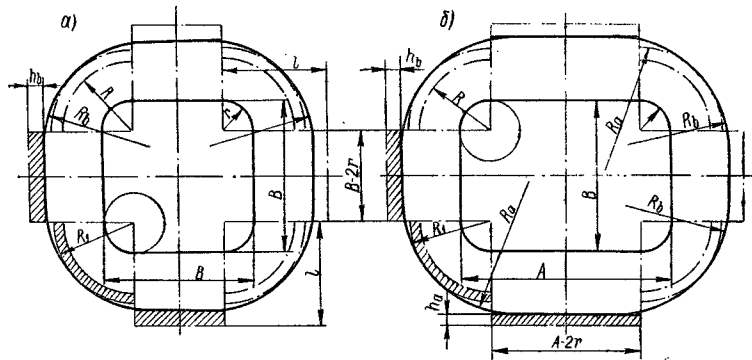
Построение формы заготовки для вытяжки невысоких коробок с относительно большими радиусами угловых закруглений (область IIb, рис. 87); а — для квадратной; б — для прямоугольной коробки
